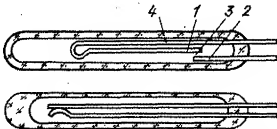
Замыкающийся (вверху) и размыкающийся герконы с выводами, направленными в одну сторону: 1 и 4 — прямой и обратный участки подвижной контакт-детали; 2 — неподвижная контакт-деталь; 3 — межконтактный зазор
